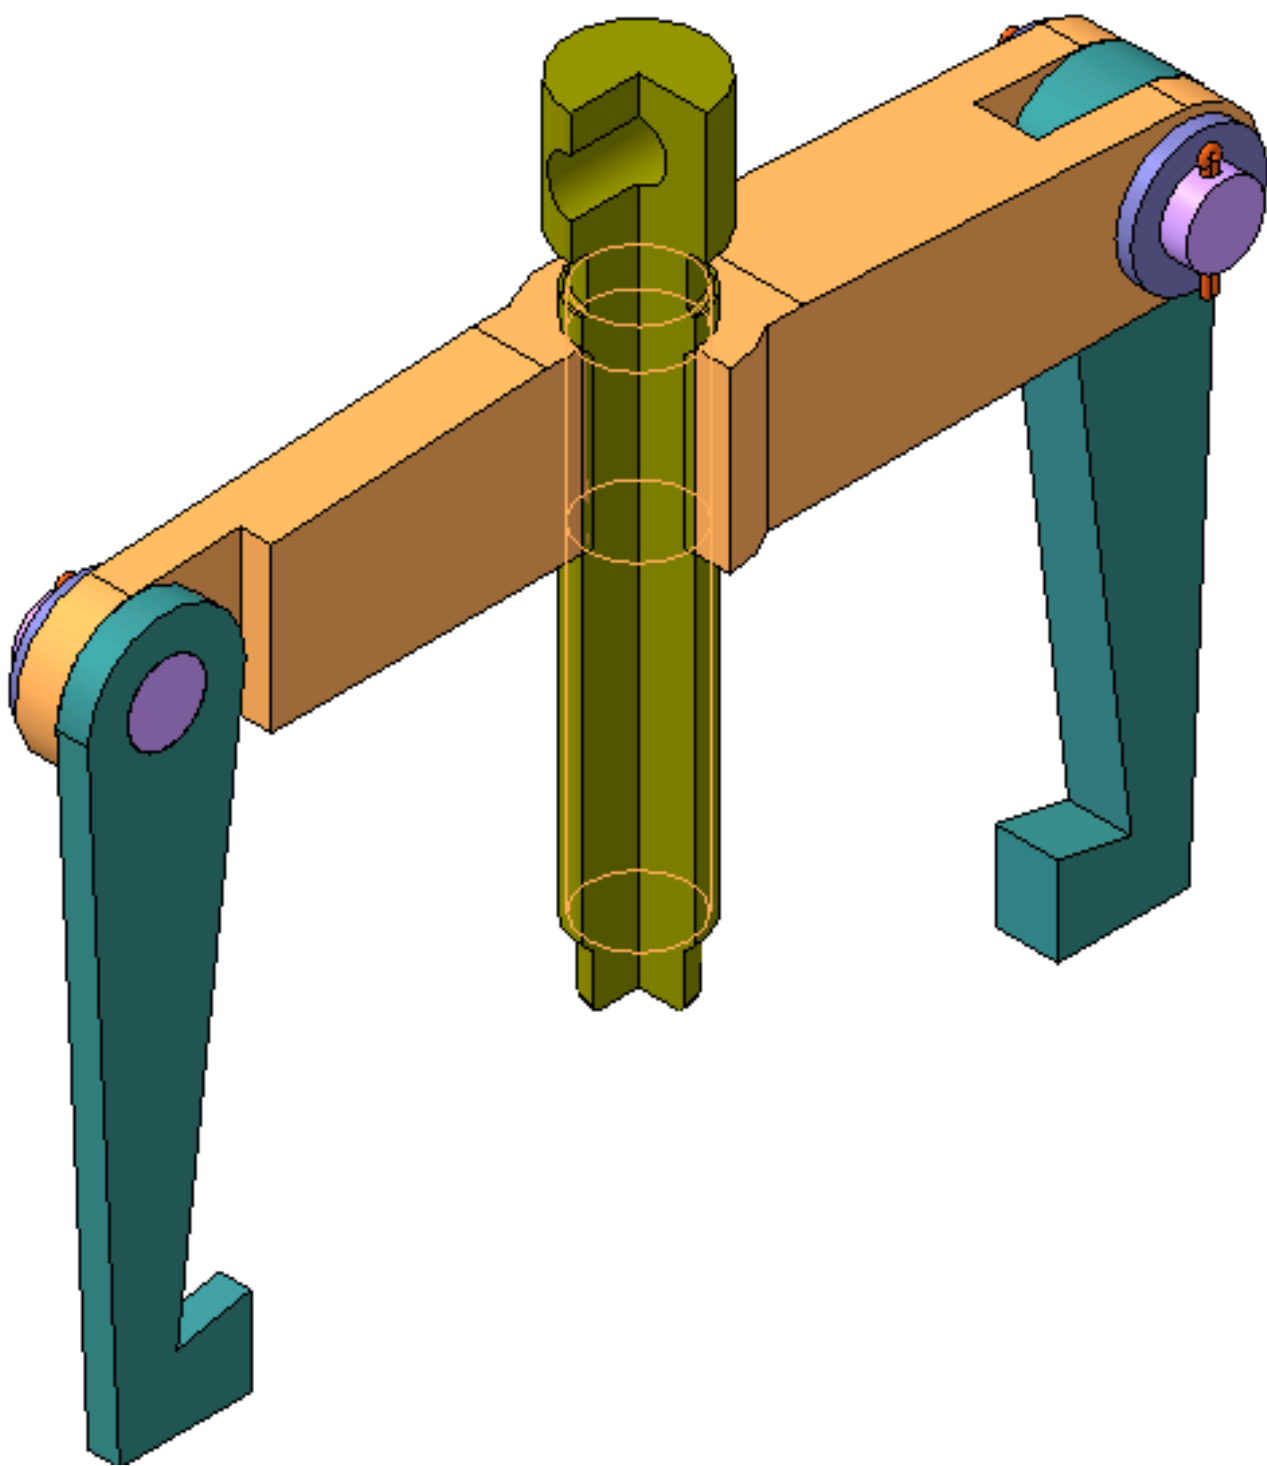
3D-модель сборки изделия «Съемник-2» (варианты 17, 37)
